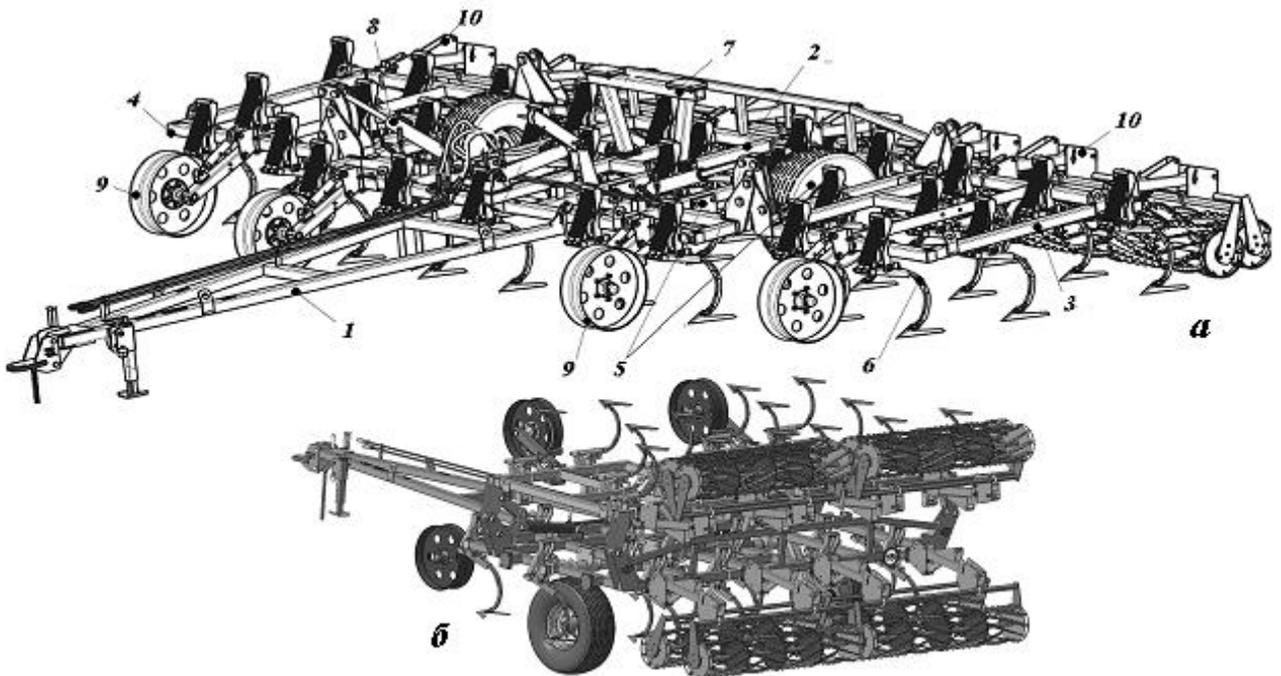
Широкозахватный культиватор КППУ-8:
